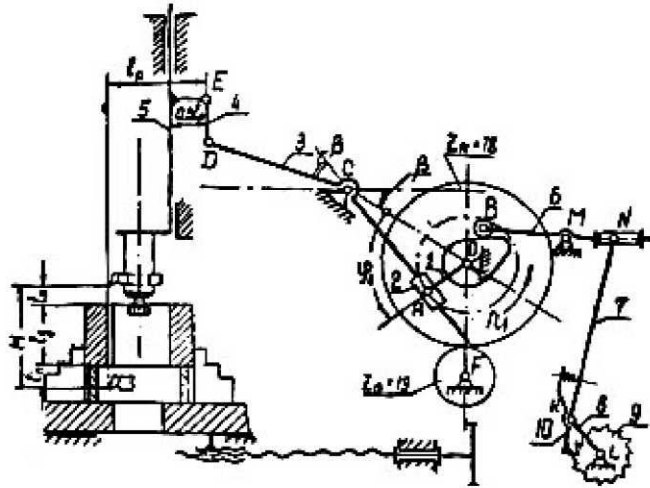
Схема кривошипно-кулисного механизма движения резца и кулачкового механизма подачи стола долбежного станка
